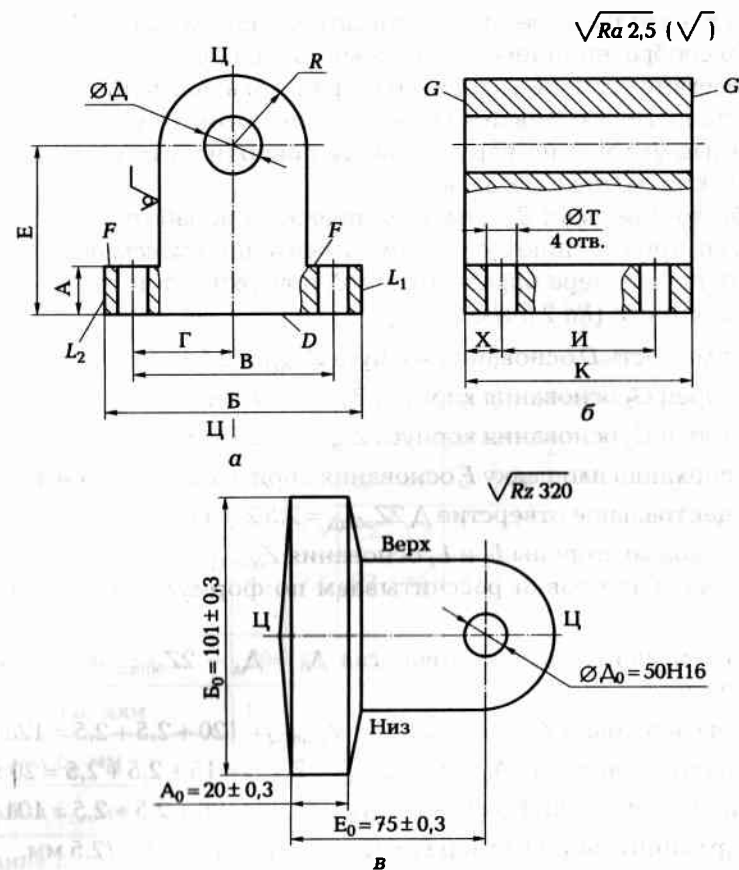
Деталь — корпус (а) и заготовка детали (б)
